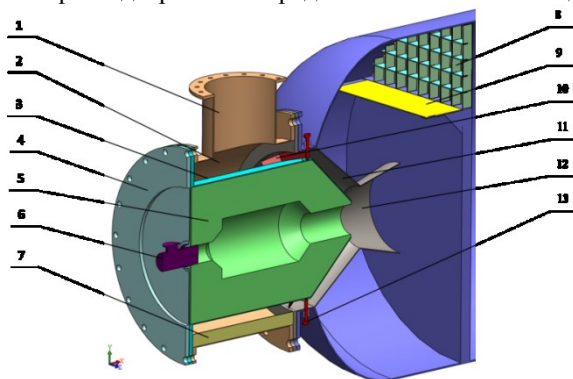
Принятый вариант конструкции проточной части реактора-подогревателя.
